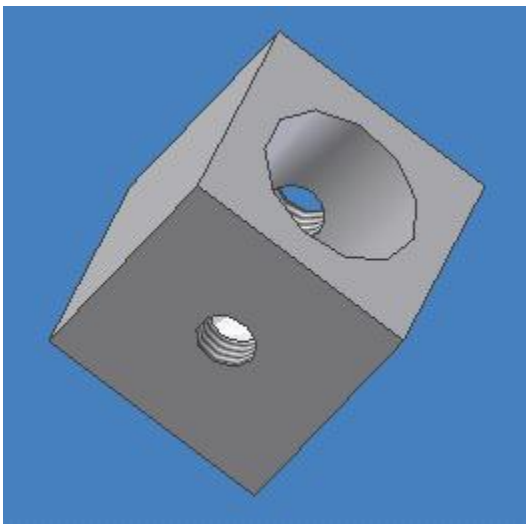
Pieza A2 . Se observa el mecanizado aplicado a 24 piezas según el plano AND00 - 0201
